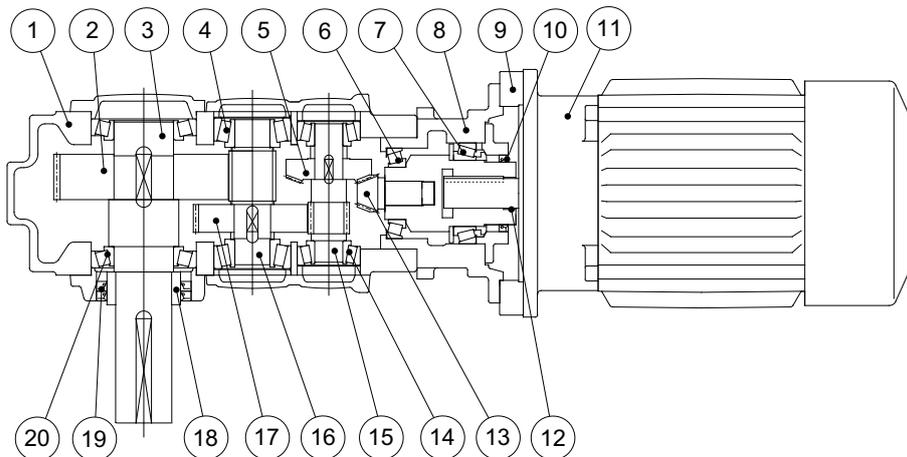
Getriebemotor mit rechtwinkliger Wellenanordnung
